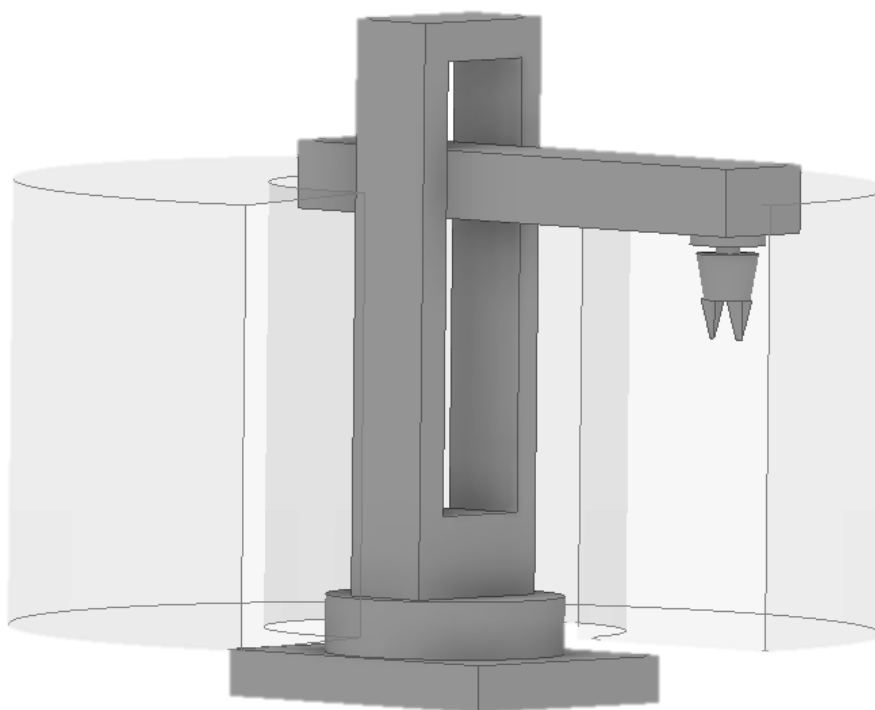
Циліндричний тип маніпулятора з виділеною робочою зоною
